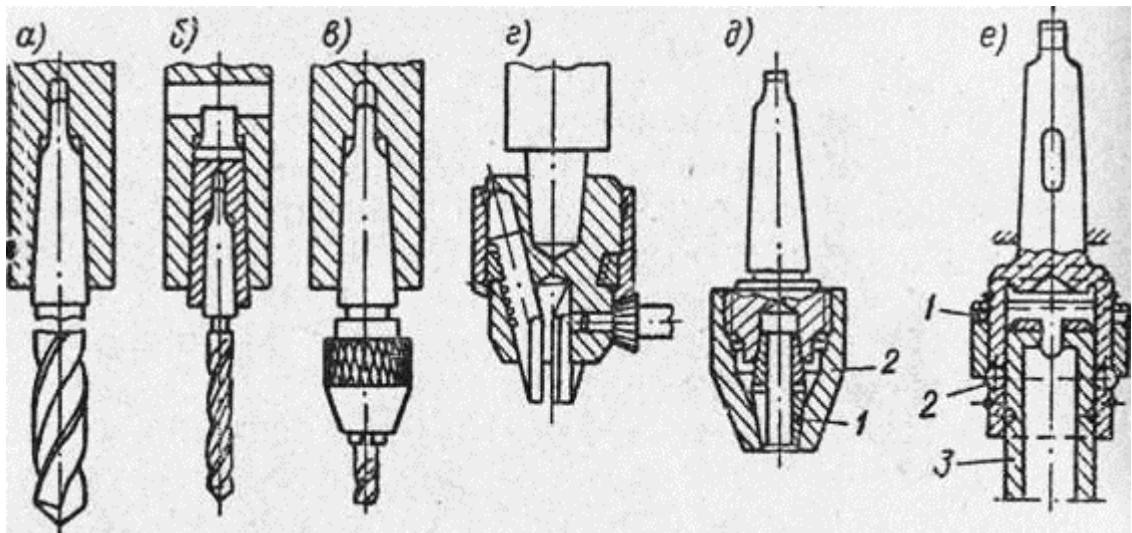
Способы закрепления режущих инструментов и патронов в шпинделе станка
